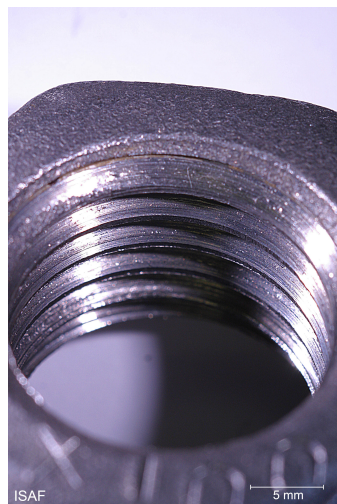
Gewindeprüfkörper axial belastet mit 100kN (Mutter)
